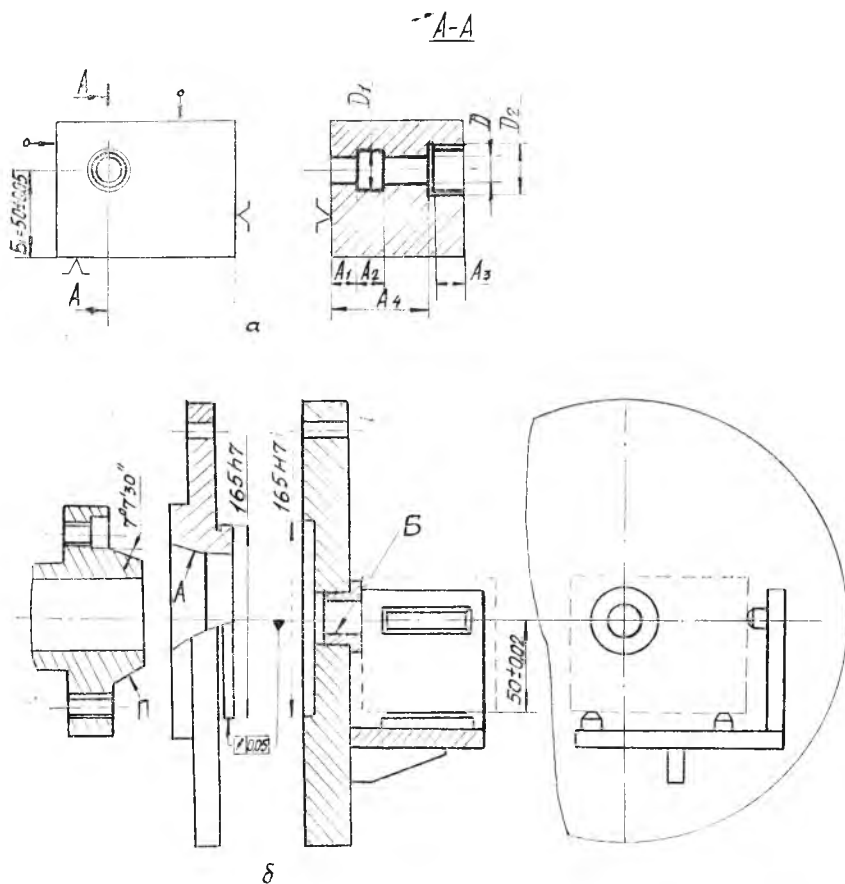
К расчету точности обработки в приспособлении на револьверном станке: а — операционный эскиз; б — приспособление
